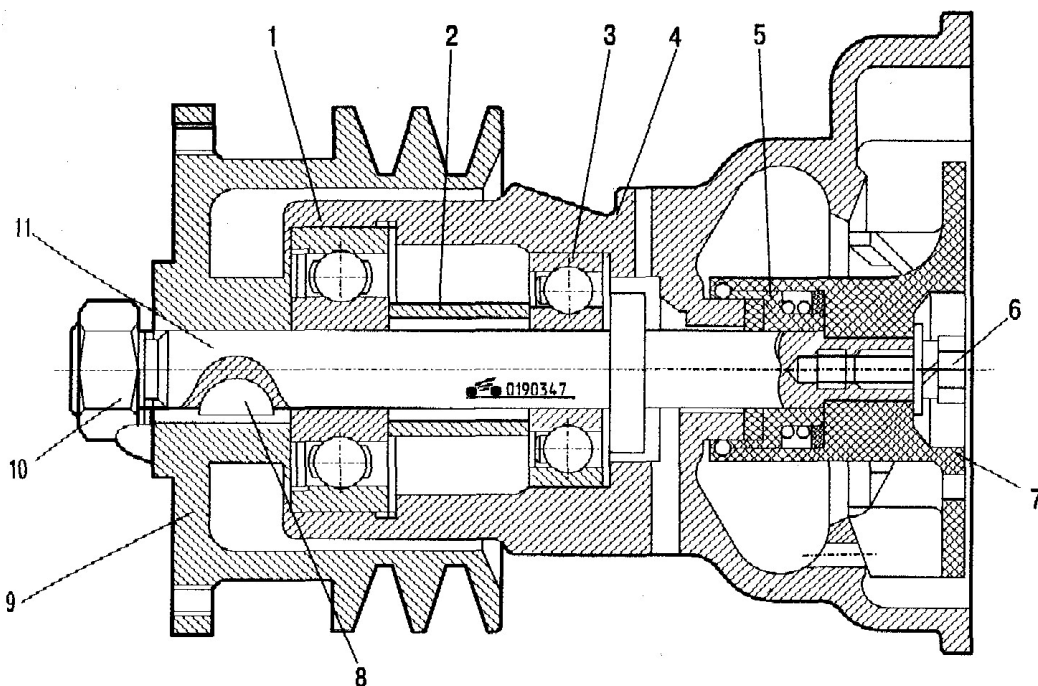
Жидкостной насос: 1,3- подшипники; 2 - распорная втулка; 4 - корпус; 5 - уплотнение; 6 - болт; 7 - крыльчатка; 8 - шпонка; 9 - шкив; 10 - гайка; 11 - вал
